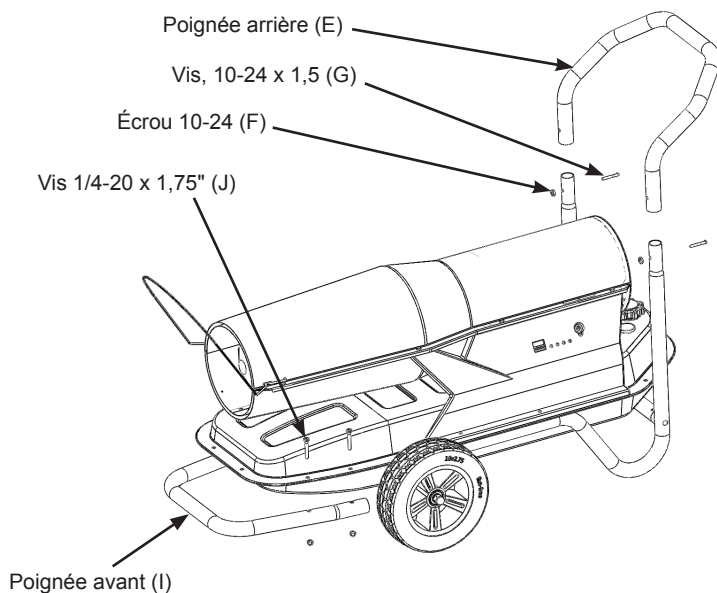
Assemblée poignée, les modèles 160, 175 et 220
